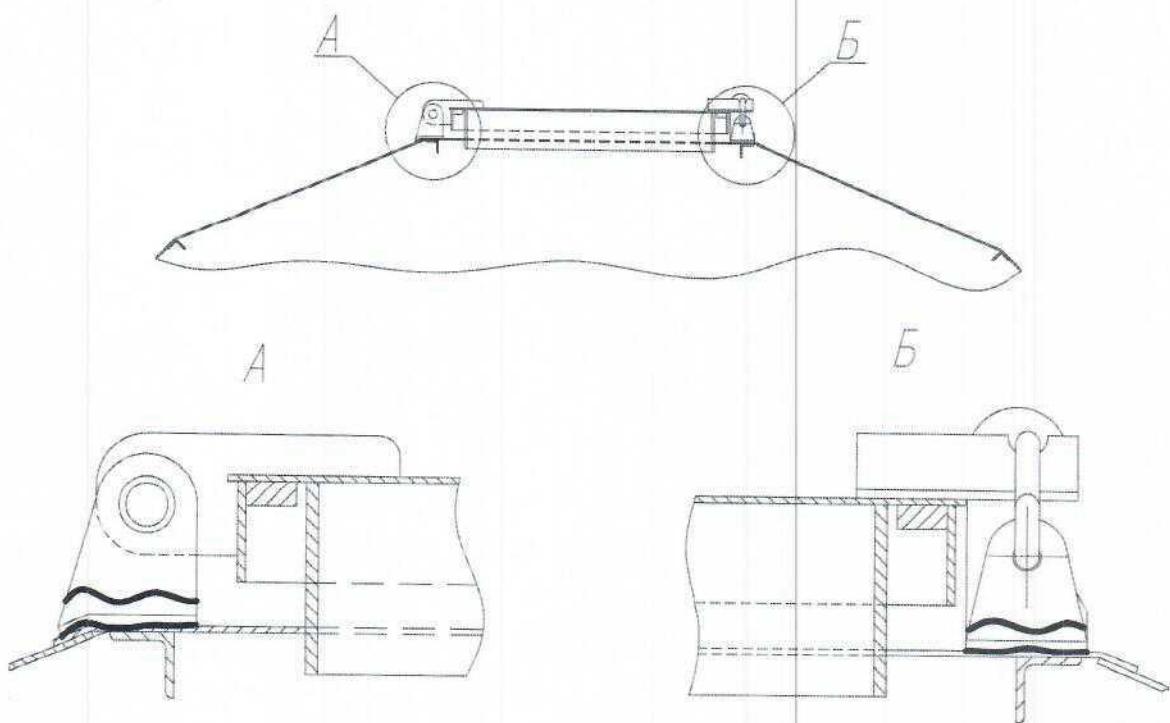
Трешины крепления крышки загрузочного люка
